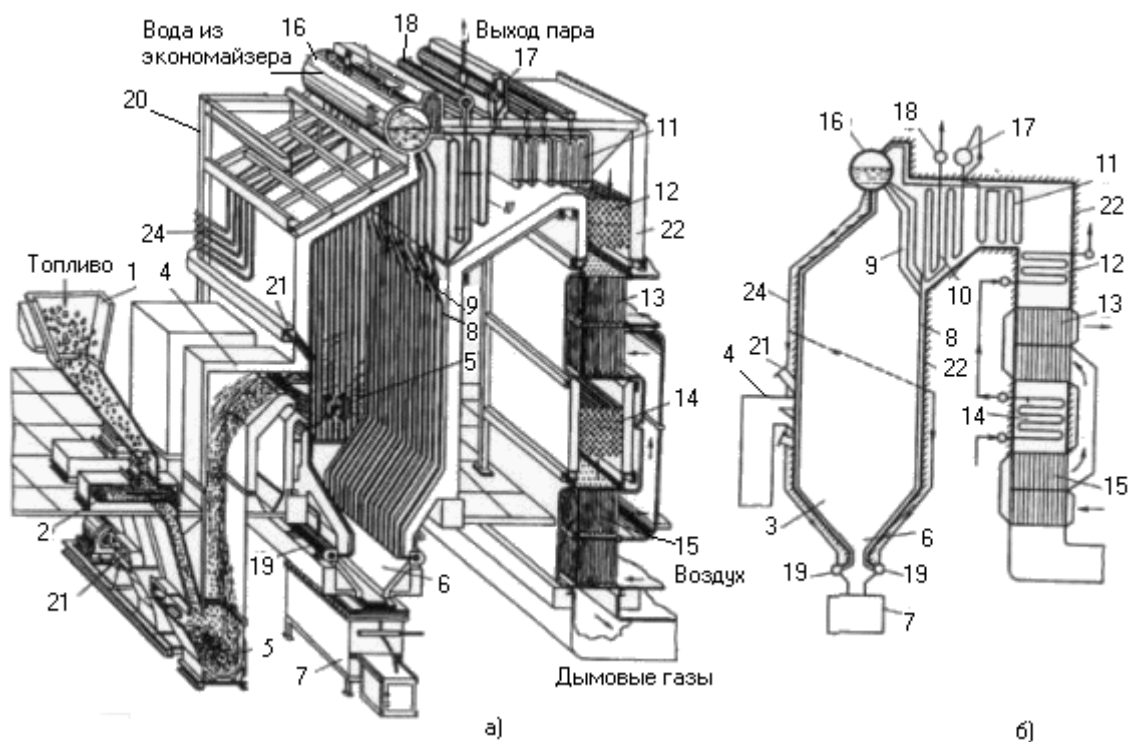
а, б. Конструктивное выполнение и схемы барабанных паровых котлов: а - для сжигания твердого топлива; б - то же, схема котла; в - для сжигания газа и мазута; г - то же, схема котла; 1 - топливный бункер (бункер сырого топлива); 2 - скребковый питатель мельницы; 3 - углеразмольная мельница с сепарационной шахтой; 4 - горелка; 5 - топочная камера; 6 - холодная воронка для удаления шлака; 7 - шлакоприемная ванна; 8 - настенные трубные экраны; 9 - многорядный пучок труб (фестон); 10, 11 - вторая и первая ступени конвективного пароперегревателя; 12, 14 - то же конвективного экономайзера; 13, 15 - то же воздухоподогревателя; 16 - барабан; 17 - регулятор перегрева пара; 18 - выходная камера пароперегревателя; 19 - нижний коллектор топочного экрана; 20 - каркас котла; 21 - короб подвода горячего воздуха; 22 - обмуровка котла; 23 - горизонтальный под топки; 24 - опускные трубы; 25 - выносной циклон-сепаратор
